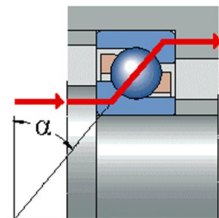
27.-Ángulo de contacto en rodamientos de bolas con contacto angular.
